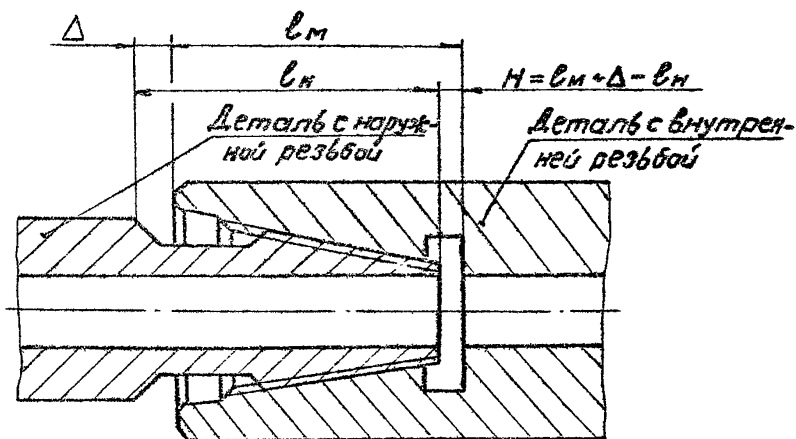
Сборка резьбовых соединений с внутренним упорным торцом.
